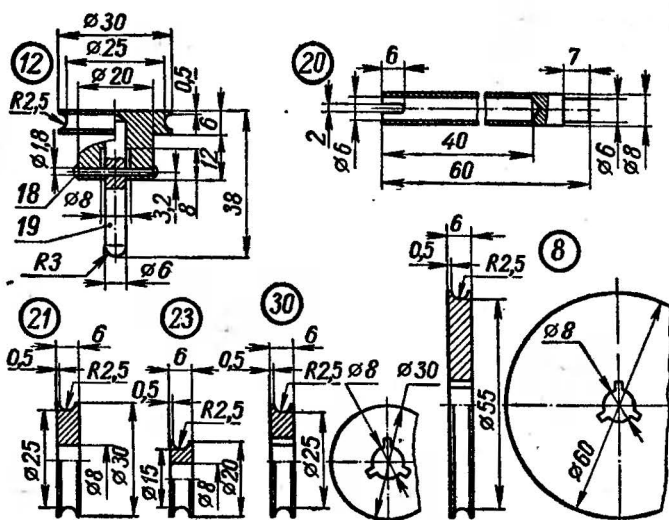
Детали механизма привода: 8 — шкив, Д16-Т; 12 — шкив, Д16-Т; 18 — штифт, проволока стальная диаметром 1,8 мм, расклепать с обеих сторон после сборки; 19 — направляющая, Ст.20, запрессовать в дет. 12; 20 — полый вал, Ст.45; 21 — шкив большой, Д16-Т; 23 — шкив малый, Д16-Т; 30 — шкив перемотки, Д16-Т
